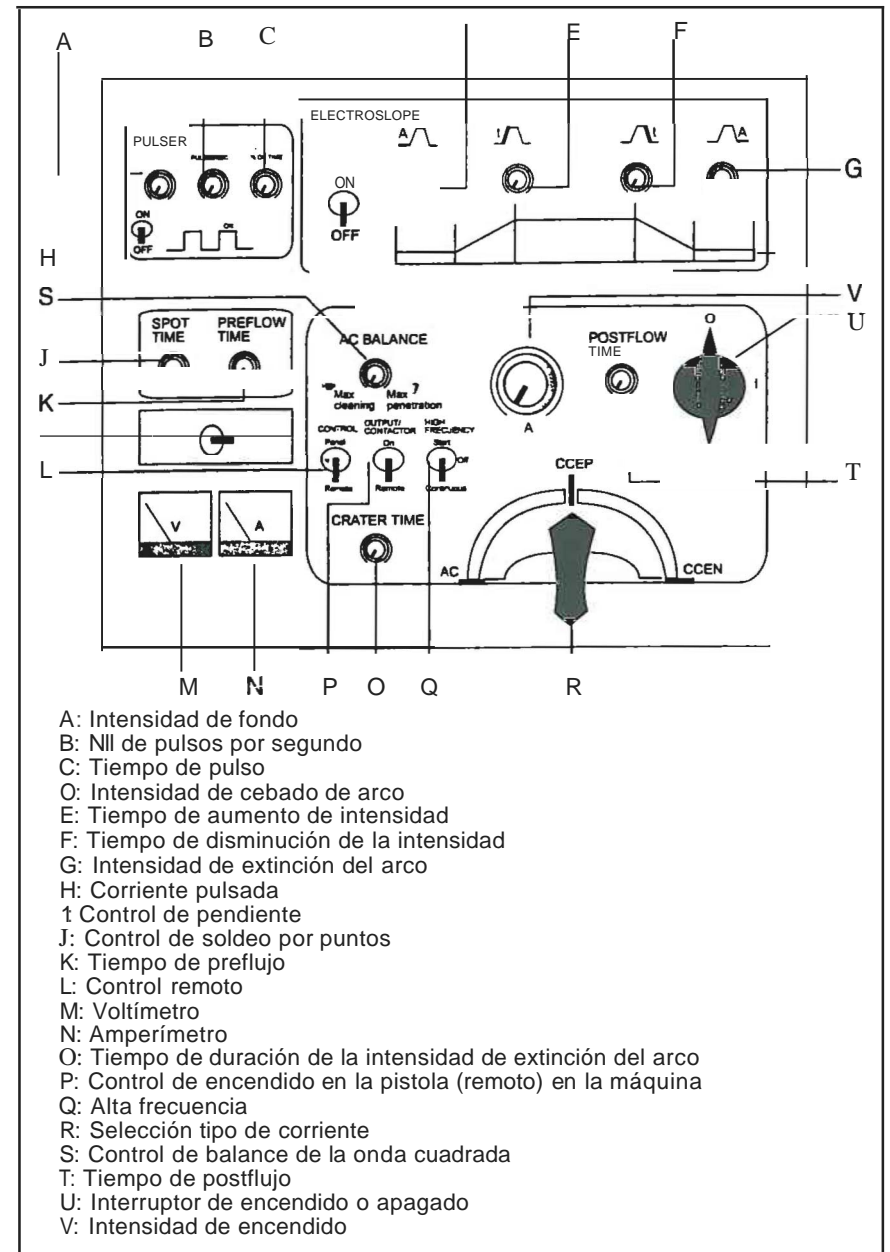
PANEL DE CONTROL DE UNA MÁQUINA TIG
